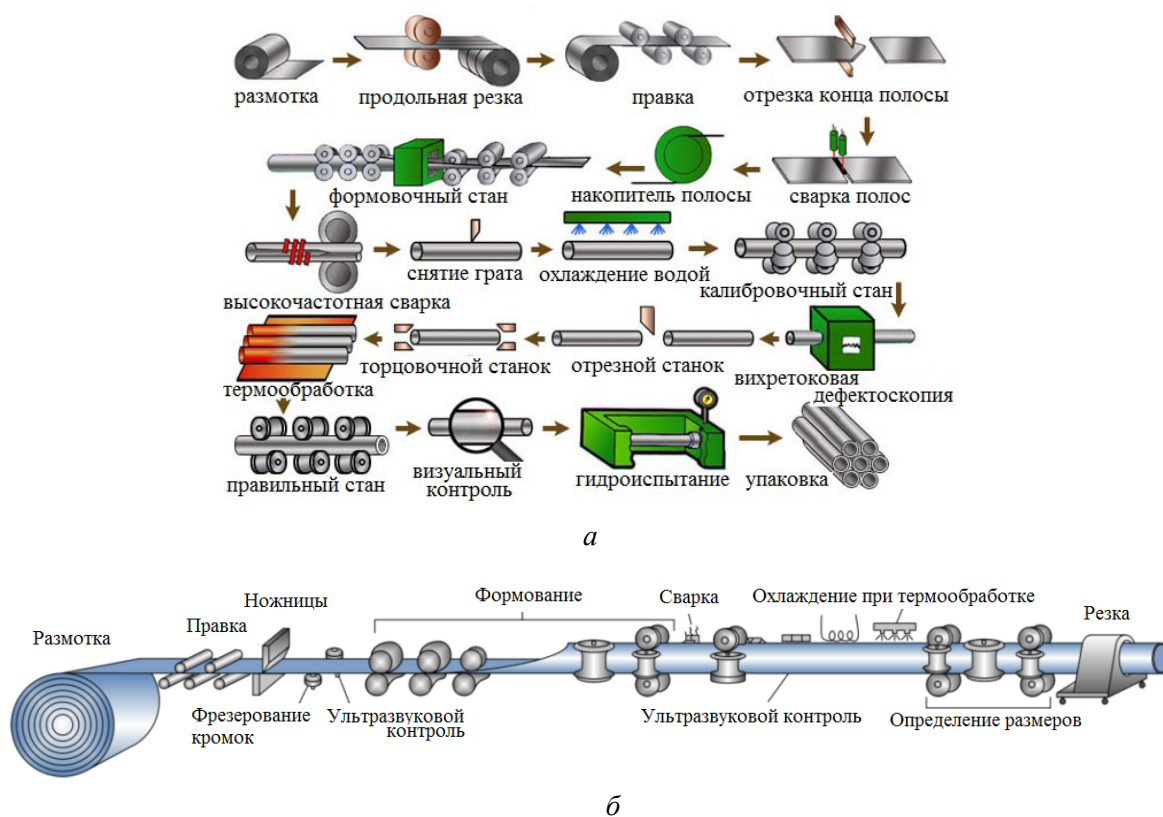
Технологии изготовления сварных стальных труб (а) и труб обычной электросваркой сопротивлением (ERW) (б)
